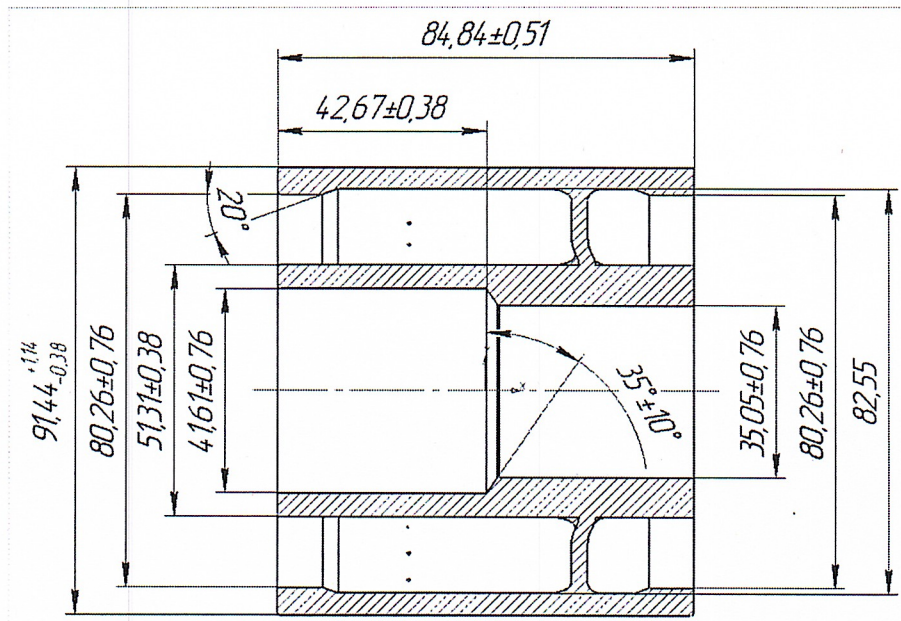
Габаритные размеры завихрителя топливной форсунки
